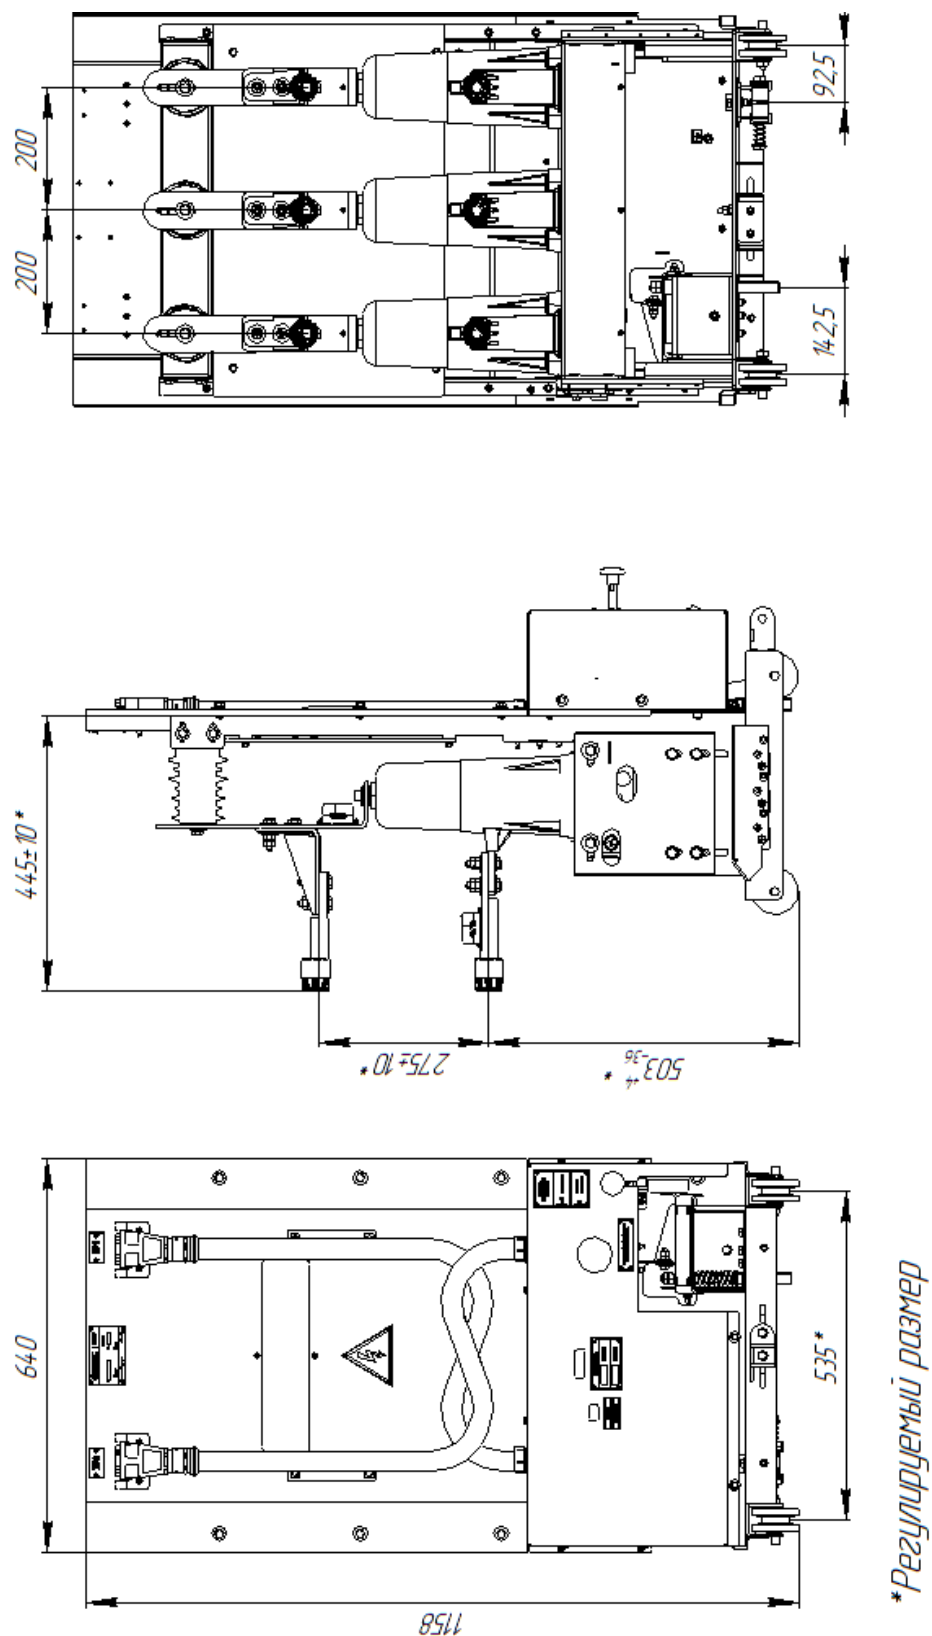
Габаритный чертеж КЭПС-ВЭ КМ-1Ф на 1000А
